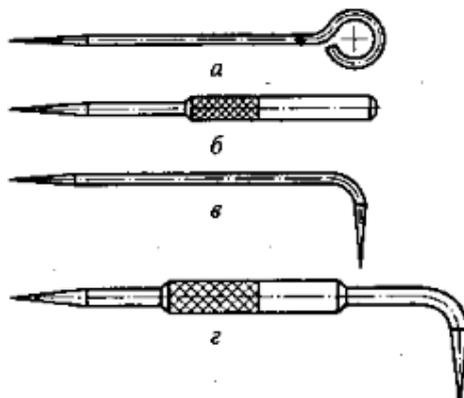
Чертилки: а – односторонняя с кольцом; б – односторонняя с ручкой; в – двусторонняя; г – двусторонняя с ручкой
